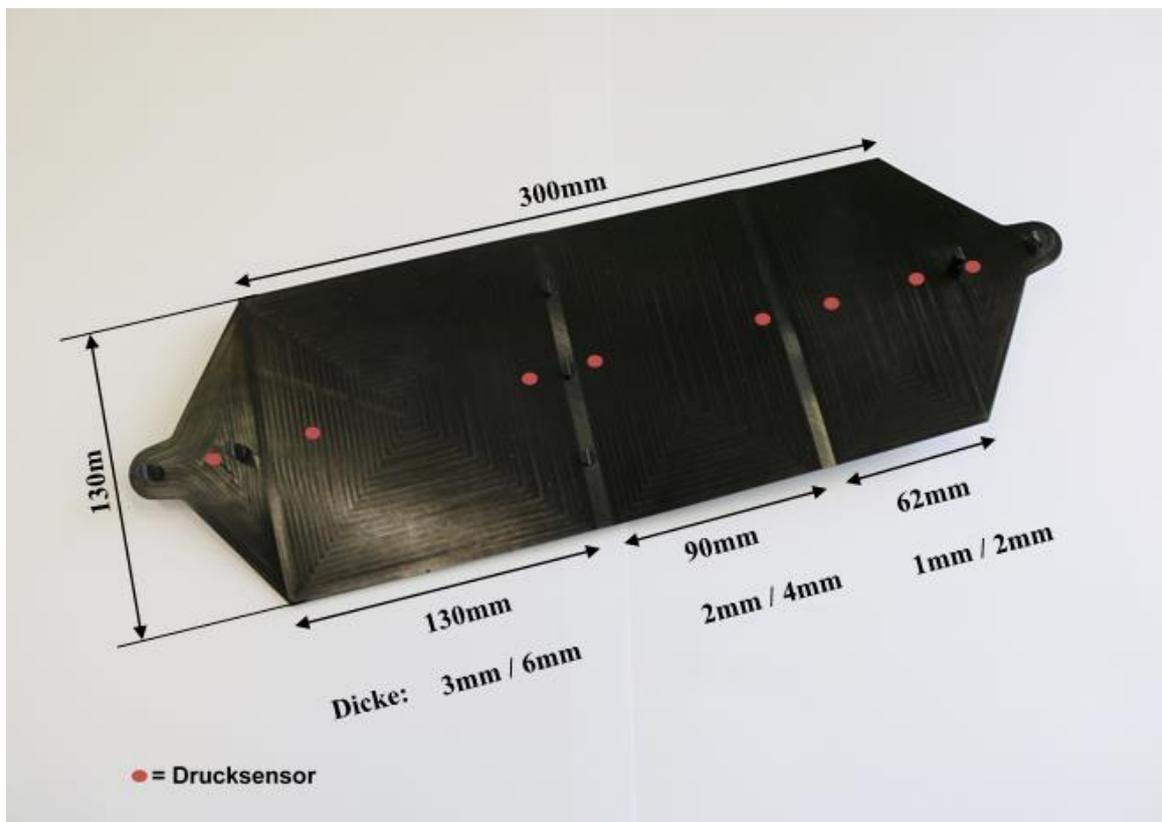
Bauteil „Stammwerkzeug“ mit Bemaßung
